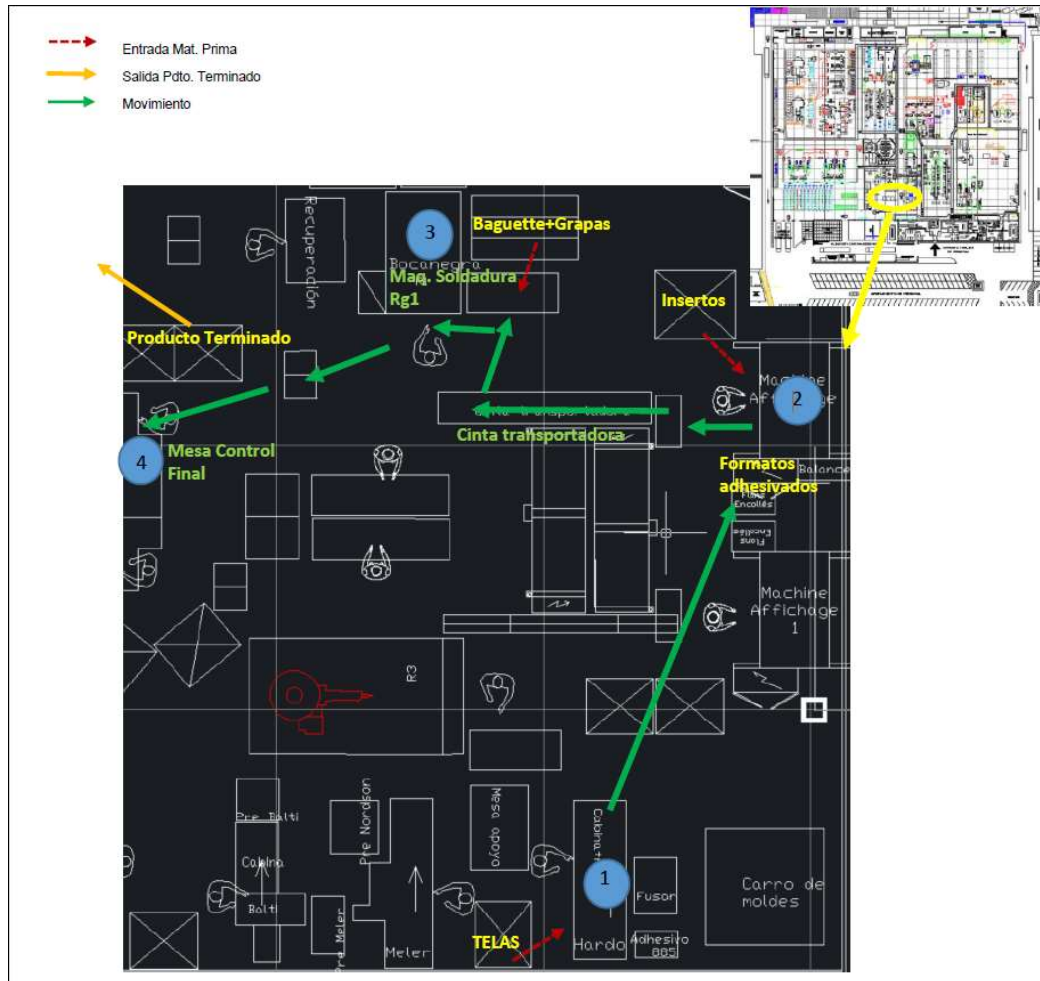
Lay-Out de la línea del Medallón KO Rg1. Fuente: (Dpto. Ingeniería GA RyA, 2021c)
